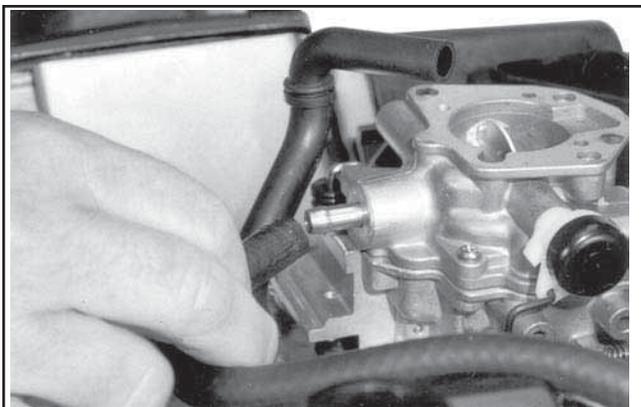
Connexion du tuyau d'entrée du carburant.
